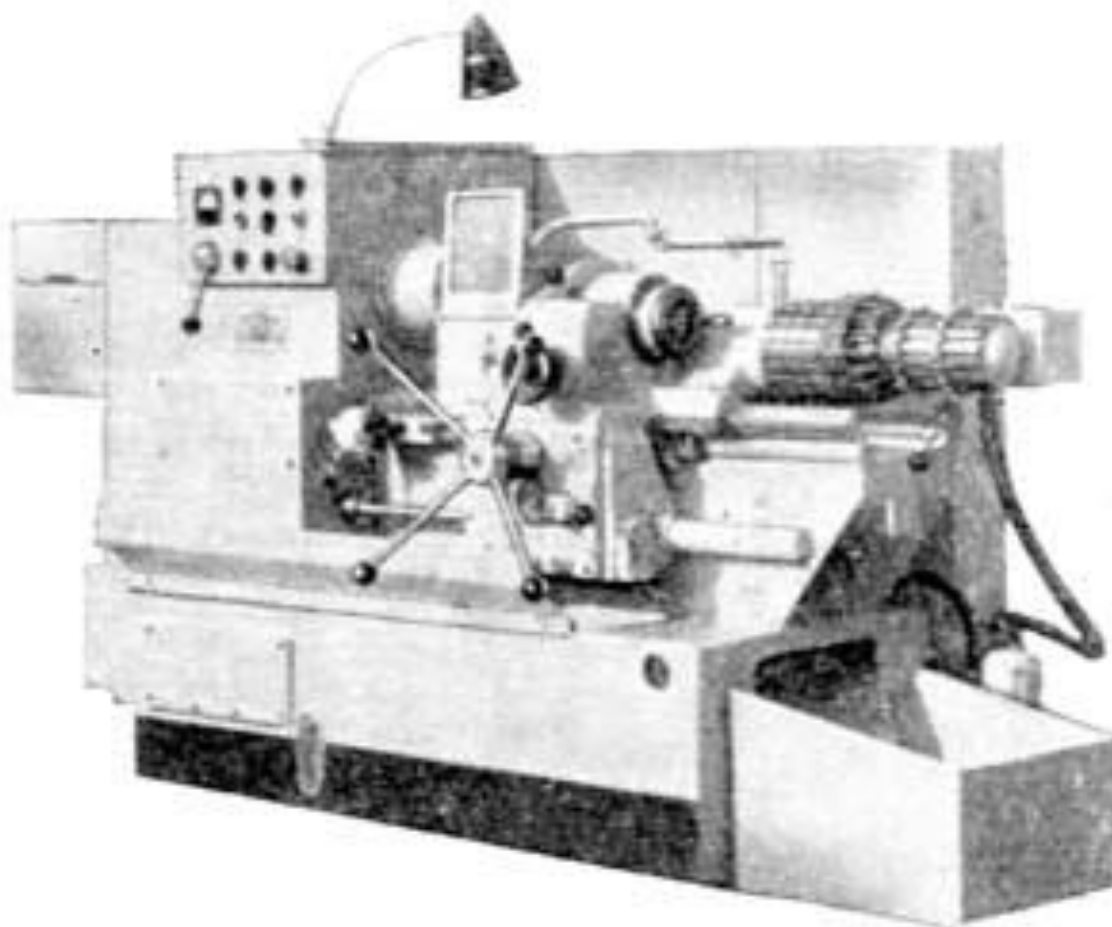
Загальний вид токарно-револьверного верстата 1341
